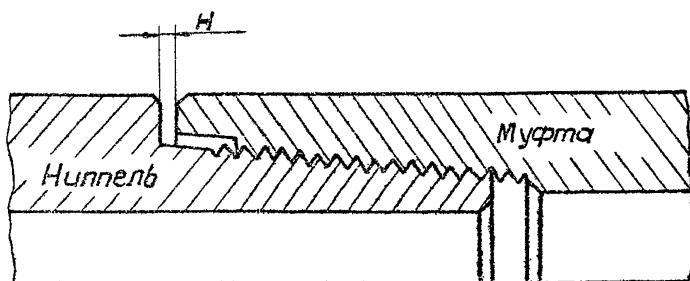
Сборка резьбовых соединений с наружным упорным торцом
